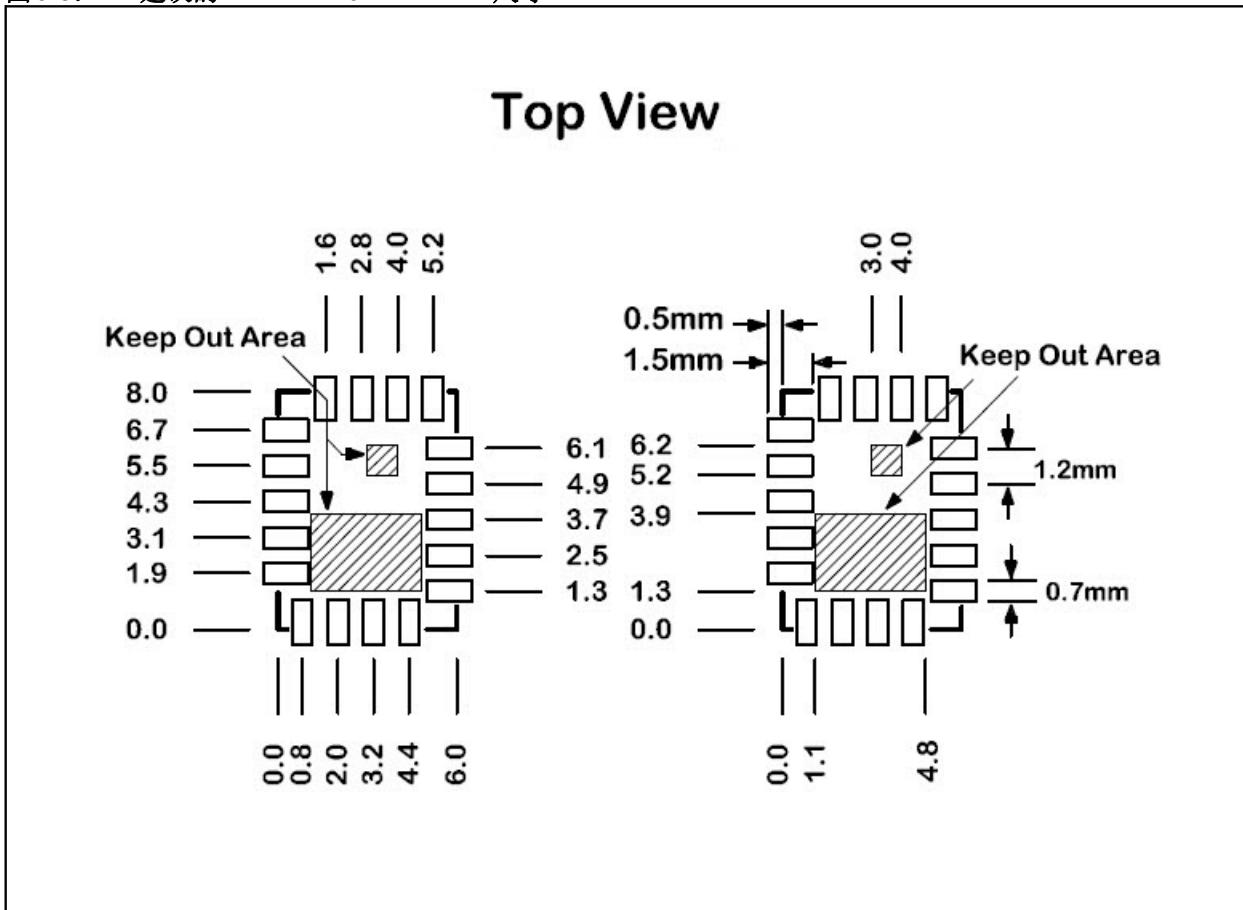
建议的 BM71BLE01FC2 PCB 尺寸
